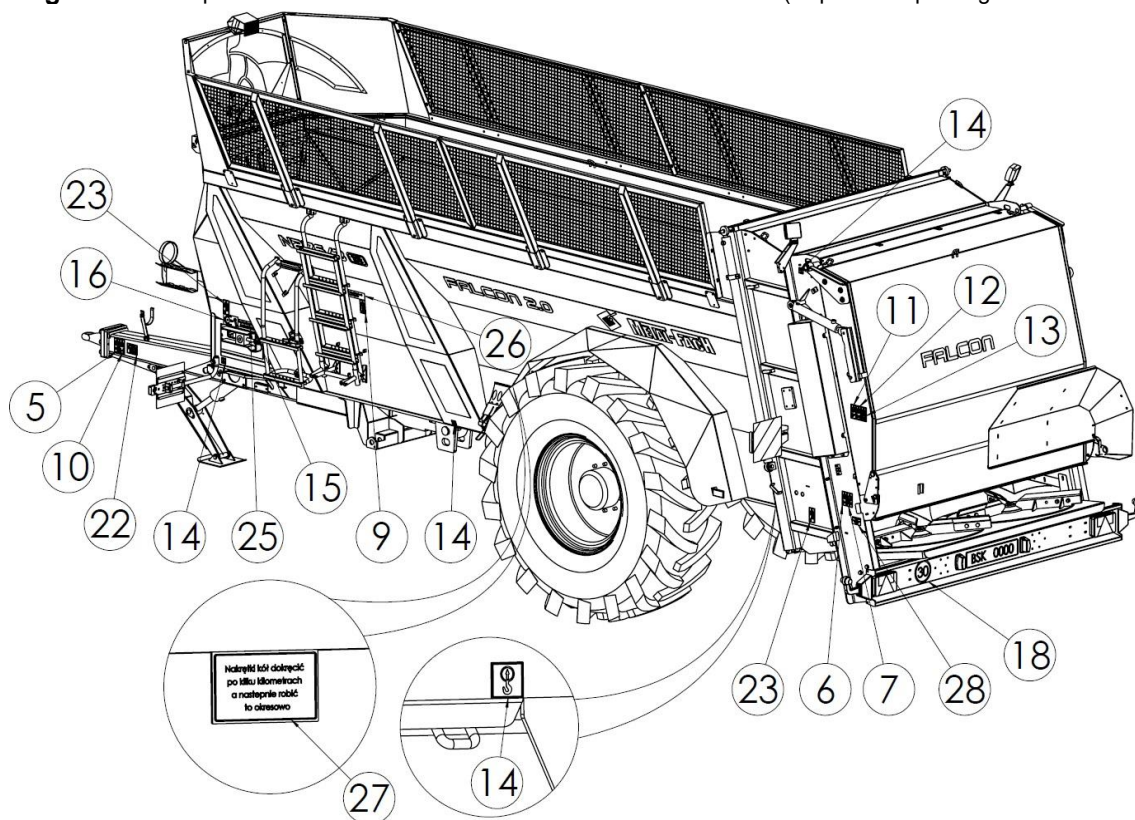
Disposition des autocollants d'avertissement et d'information (dispositif d'épandage horizontal – arrière)
